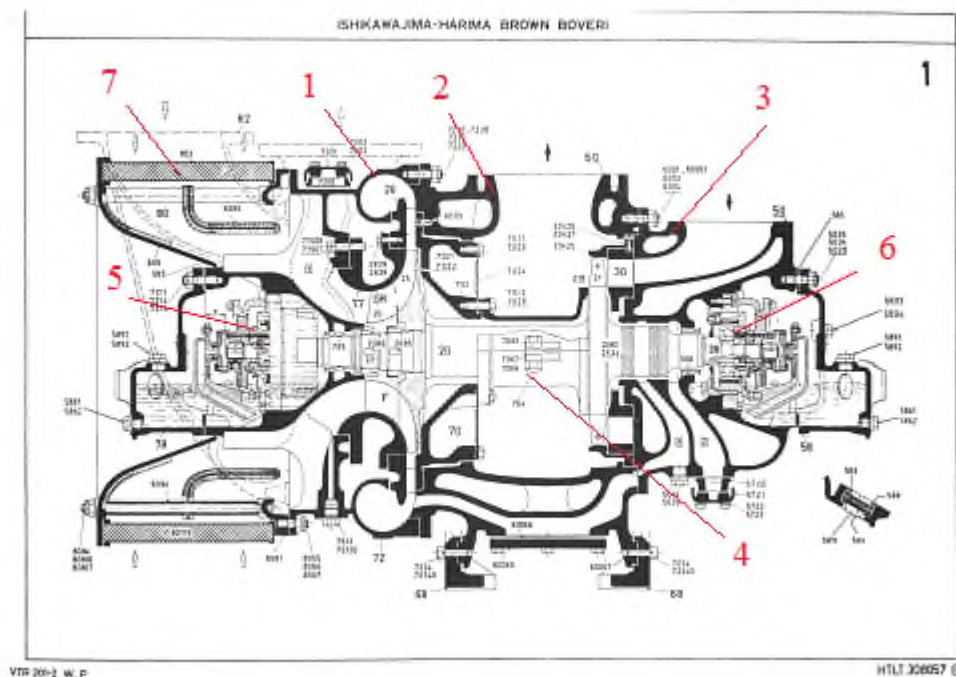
Загальний вид турбокомпресора-прототипу: 1 – корпус компресора; 2 – середній корпус; 3 – газоприймальний корпус; 4 – ротор у зборі; 5 – опорно-упорний підшипник; 6 - опорний підшипник; 7 - фільтр
